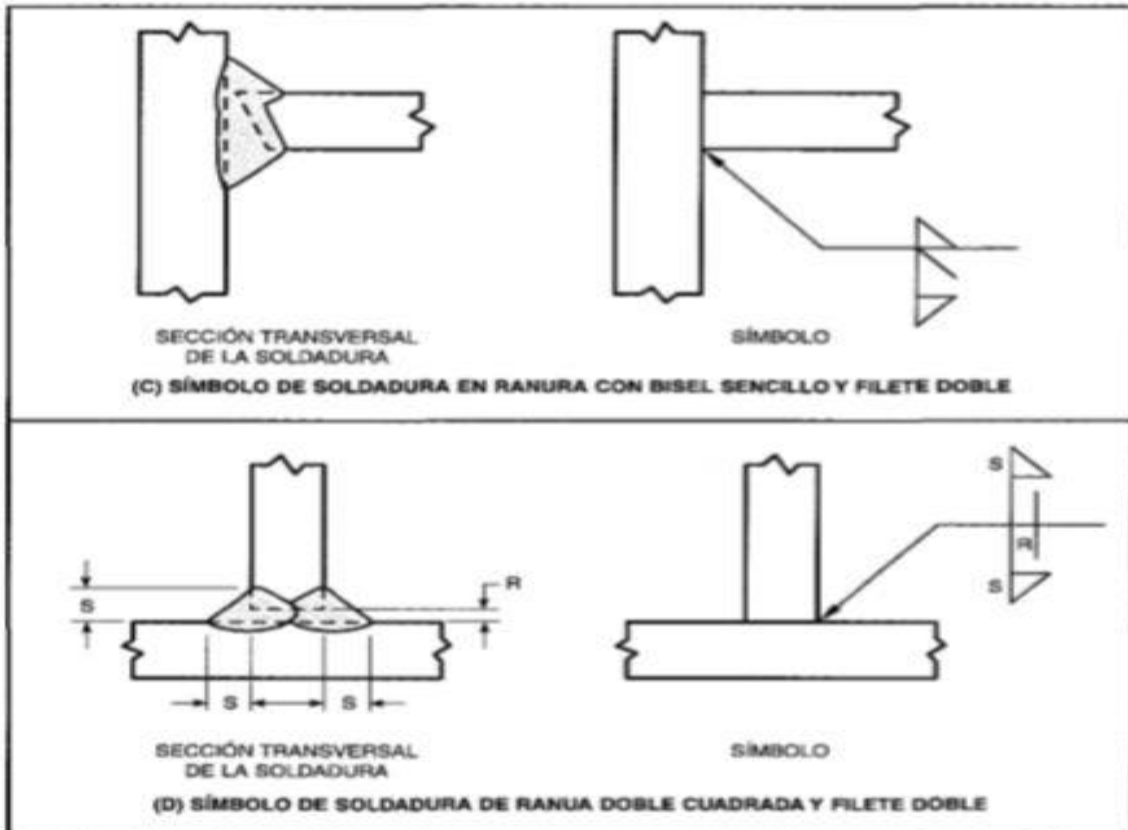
(Continuación)—Combinaciones de Símbolos de Soldadura
